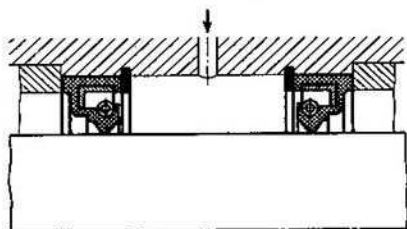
Empaquetadura sopladora con manguitos de empaque
